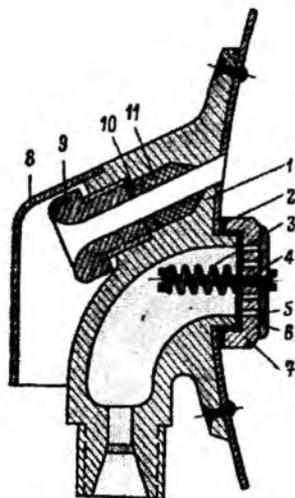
Повітряно-телефонний ввід: 1- корпус; 2- прокладка; 3- пружина; 4 -стакан; 5- тарілка клапана; 6- шкіряна прокладка; 7- корпус клапана; 8- запобіжний щиток; 9- натискна гайка; 10- упорне кільце; 11- гумова ущільнююча втулка.
